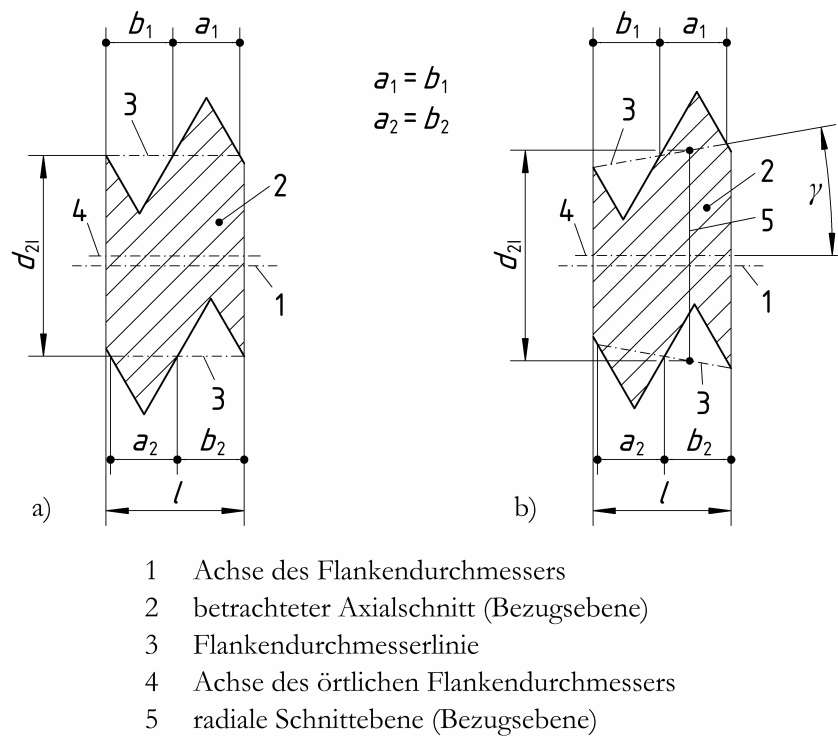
Flankendurchmesser a) eines zylindrischen und b) eines kegeligen eingängigen Außengewindes
